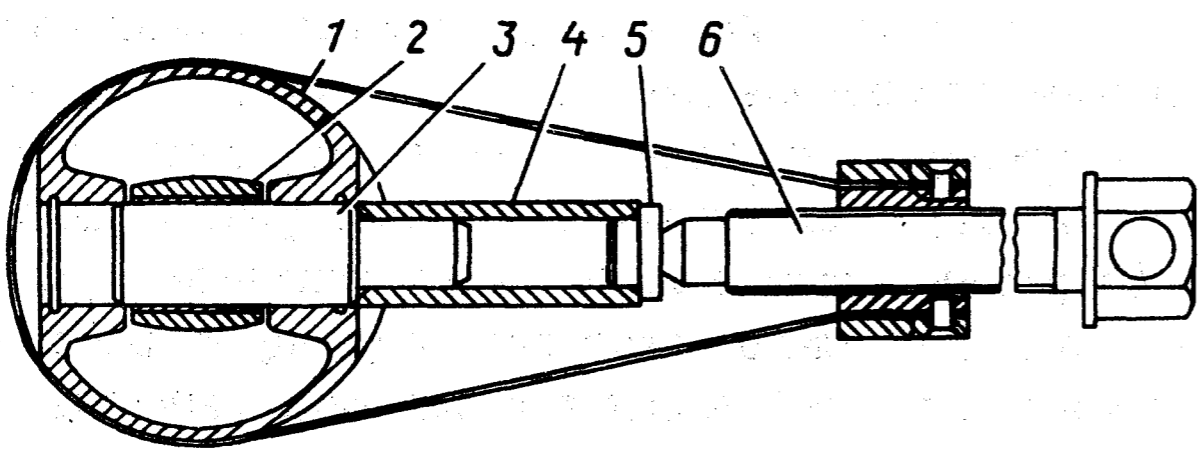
Запрессовка поршневого пальца в поршень и шатун съемником 7823-6102:
